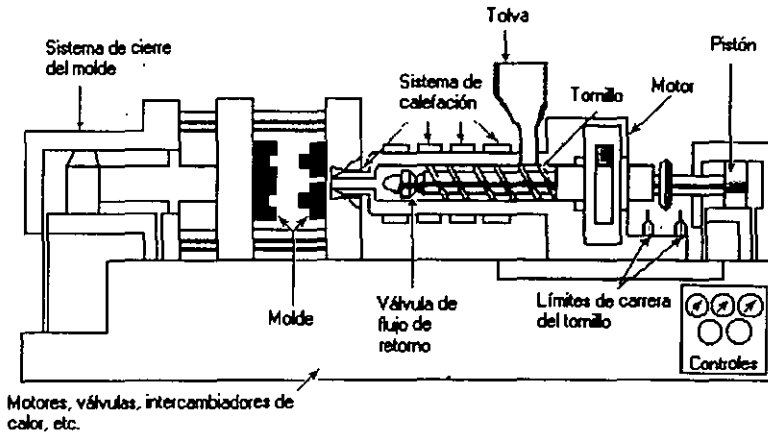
Diagrama físico de una máquina hidráulica de inyección
